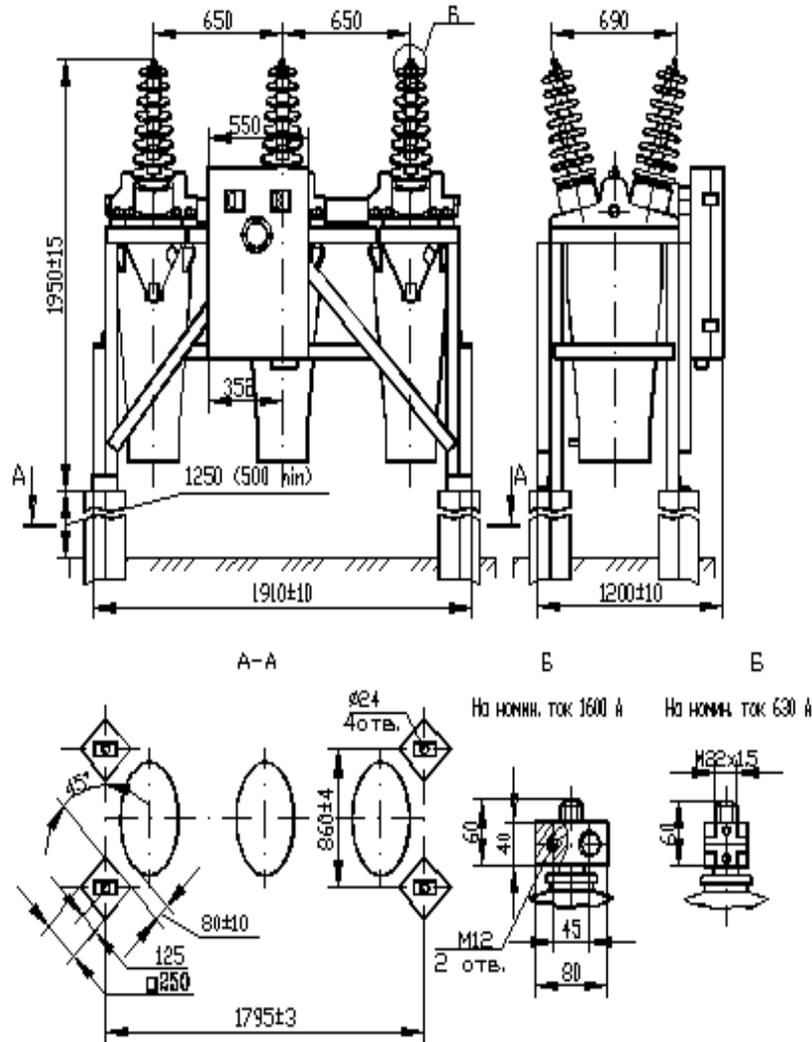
Габаритные и установочно-присоединительные размеры выключателя
